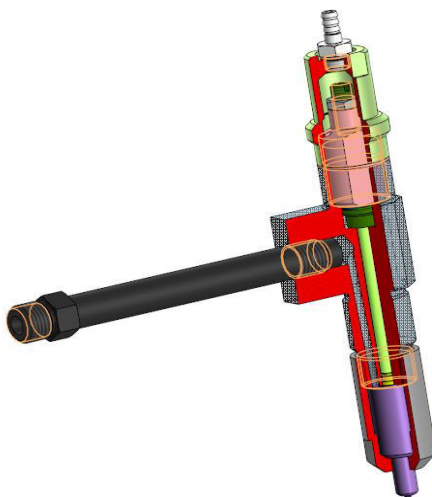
Общий вид конструкции форсунки (3D-модель)
